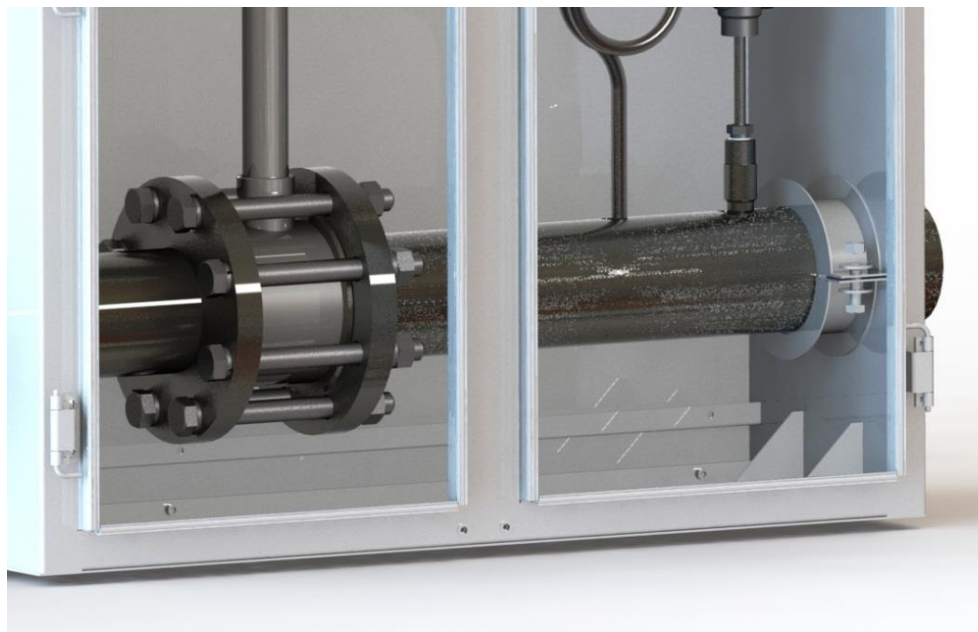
Крепление нижней полки и корпуса шкафа
